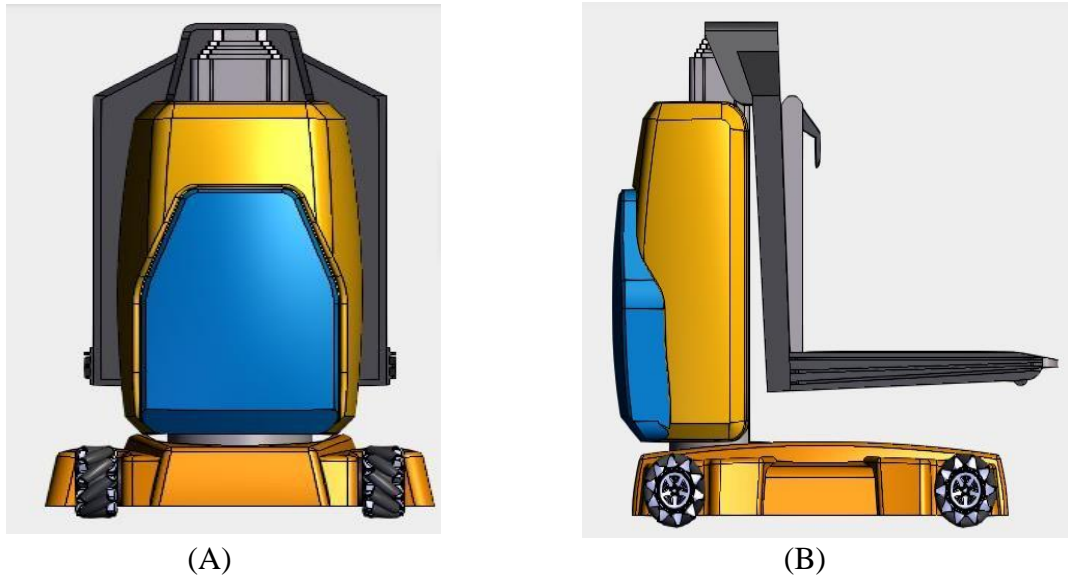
(A) Vue de face et (B) vue latérale de l'AGV
